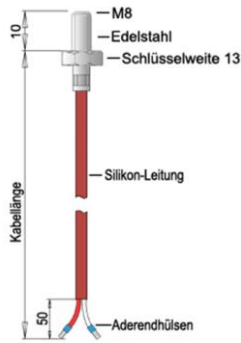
Einschraubfühler mit einem M8x10 Gewinde [Sen14]
